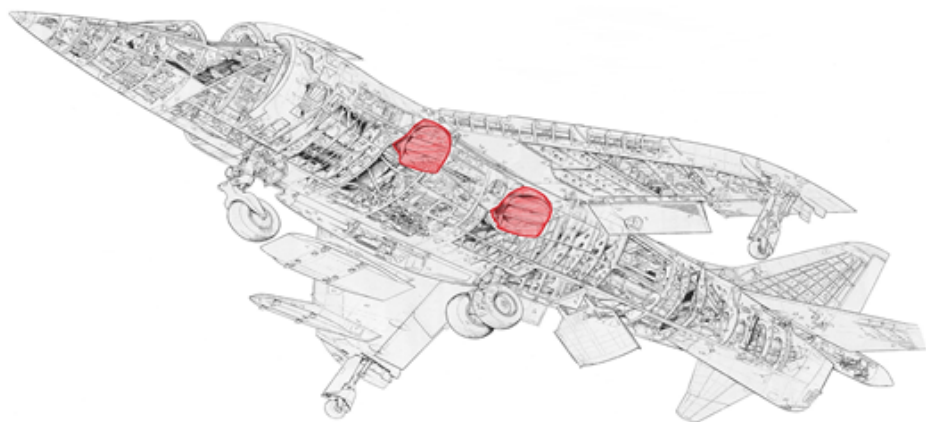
Конструкция силовой установки самолета Hawker Siddeley Harrier
